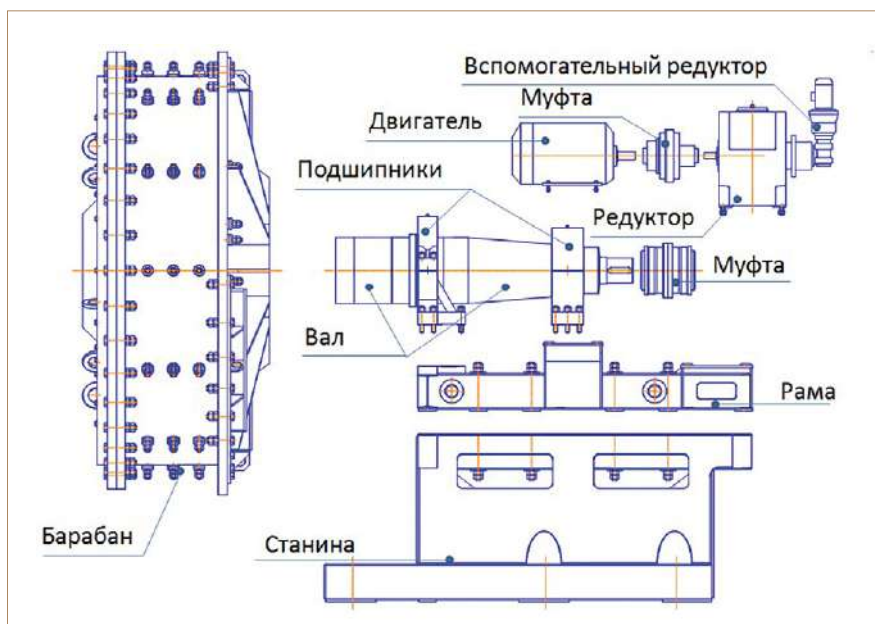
Монтажные и транспортные узлы мельницы самоизмельчения консольного типа с размерами барабанов 5.0x1.33м
